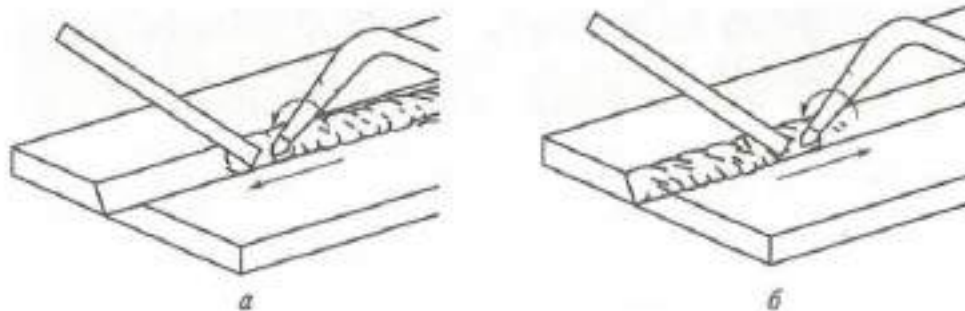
Левый (а) и правый (б) способы газовой сварки
